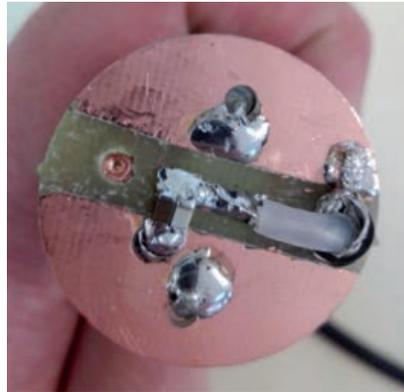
Placa PCB FR4 tallada con cable alimentación y condensadores 0805 SMD soldados
